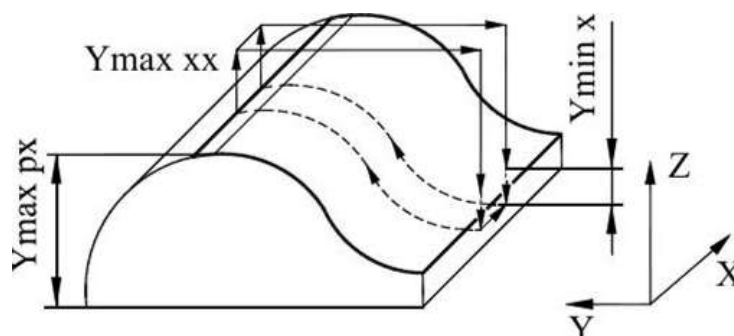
Траєкторія фрезерування криволінійної поверхні.
